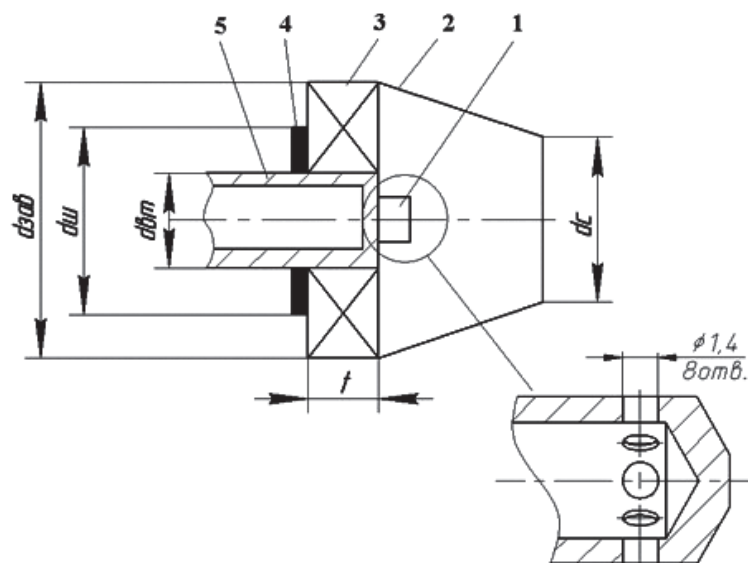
Схема вихревой форсунки: 1 — распылитель; 2 — конфузурный насадок; 3 — лопаточный завихритель; 4 — дросселирующая шайба; 5 — втулка завихрителя
